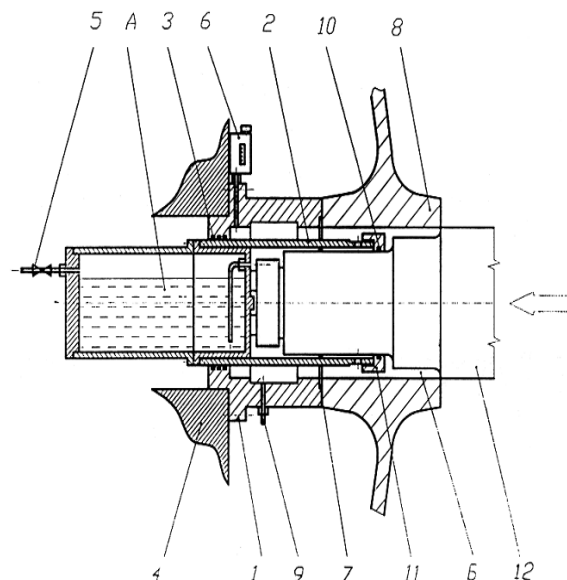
Устройство для смазки поверхностей сопряжения осей и колёс при механической запрессовке колёсных пар
